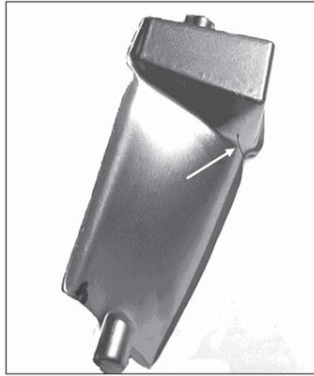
Заготовка лопатки авіаційного двигуна з дефектом у вигляді закова (прострілу)
